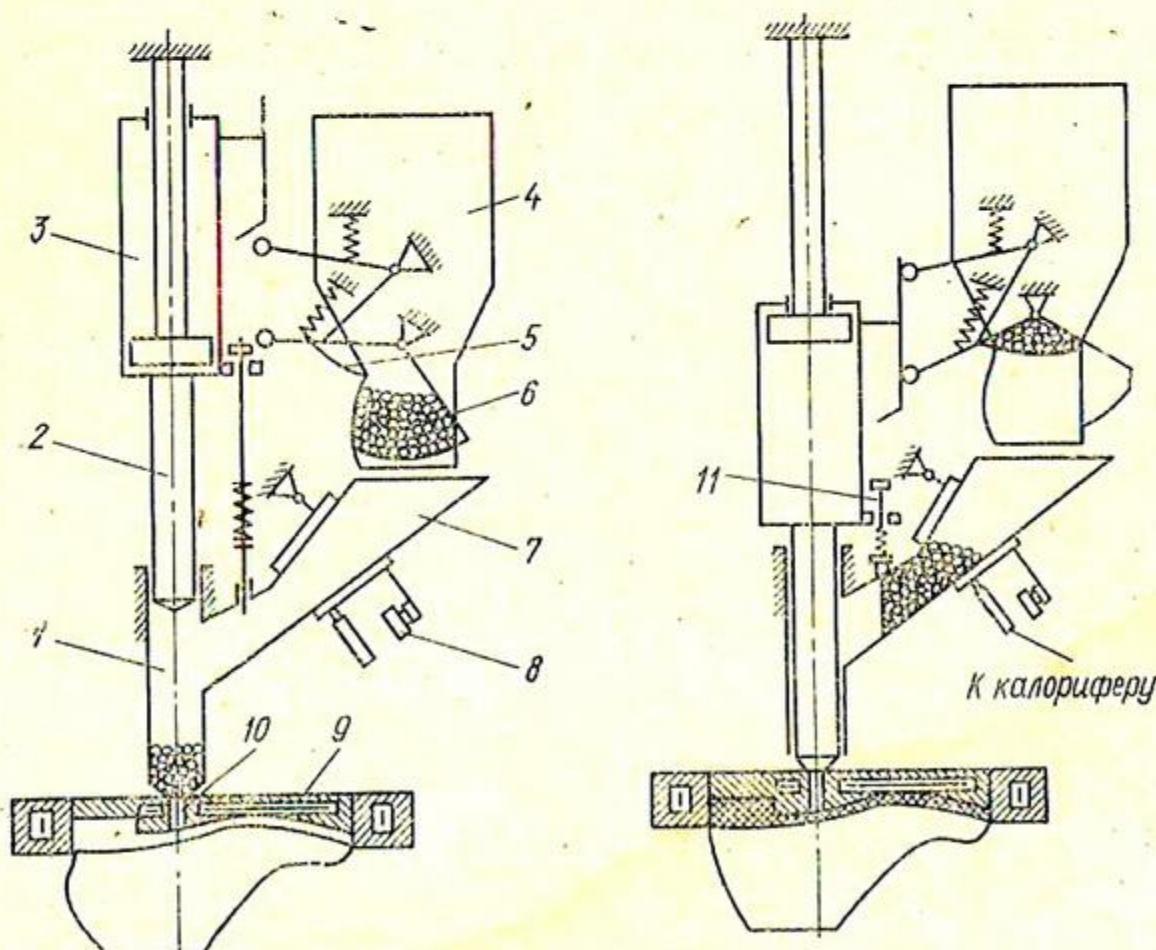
Схема литьевого устройства пресса ЛПГВ-1-О
